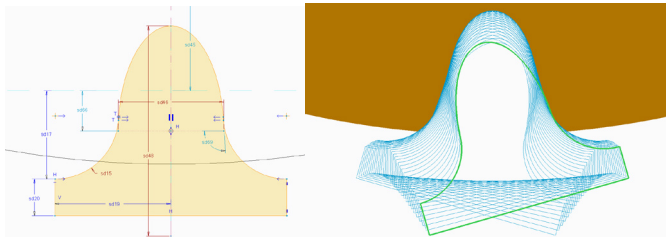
Werkzeug mit parabelförmigen Flanken und dazugehörige Hüllschnitte
